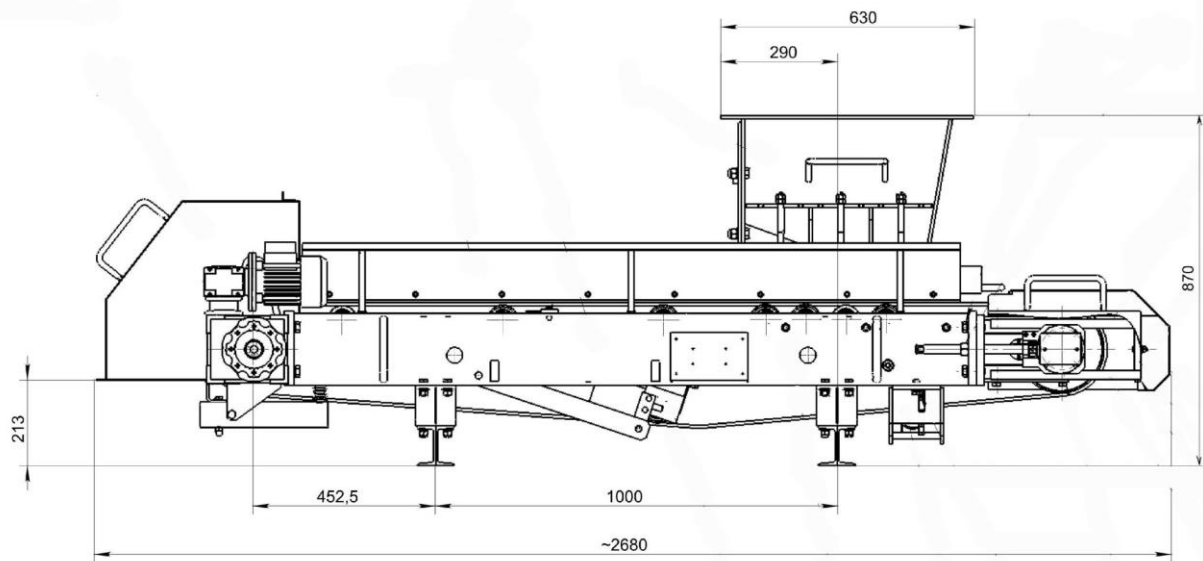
Стрічковий дозатор SWEDA DWL-1000
